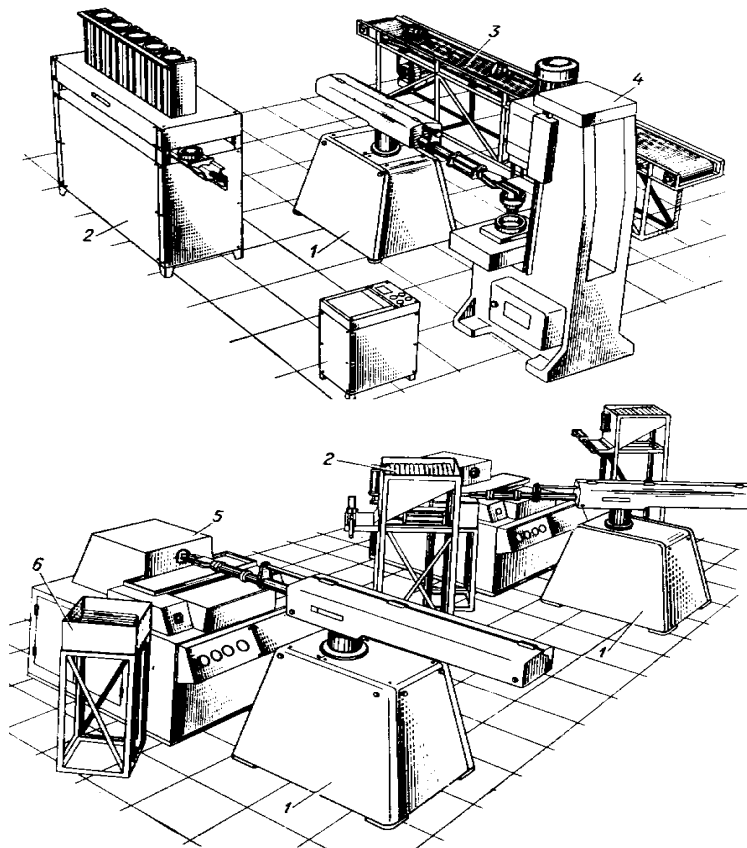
Використання робота SR-10 в автоматичних лініях свердління отворів і нарізування канавок: 1 – робот; 2 – пристрій подачі заготовок; 3 – конвеєр; 4 – свердлильний верстат; 5 – верстат для нарізування канавок; 6 – ящик для деталей
